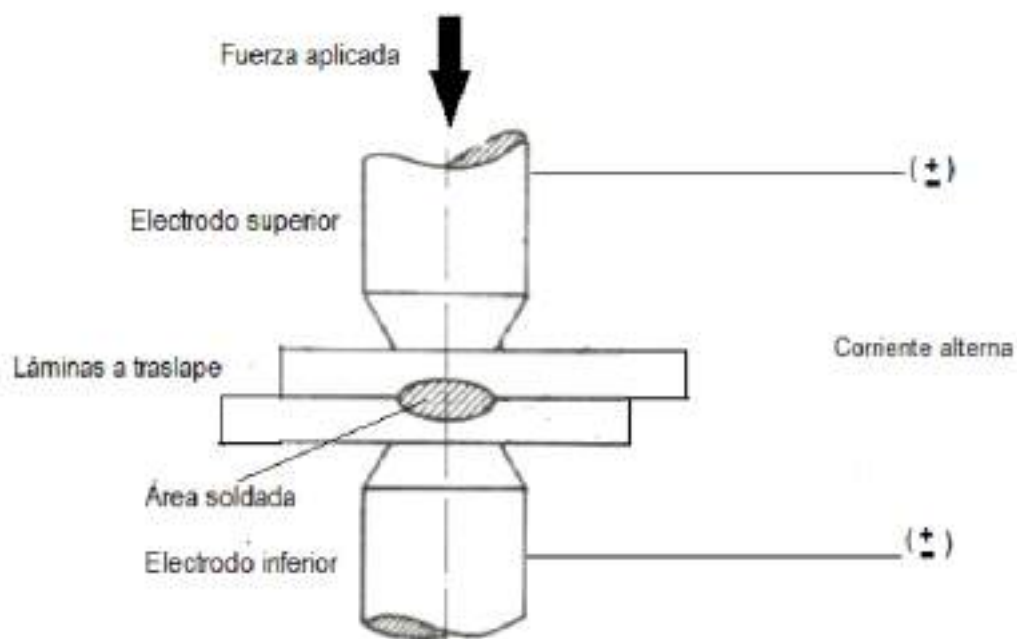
Descripción del proceso de soldadura por resistencia eléctrica.
